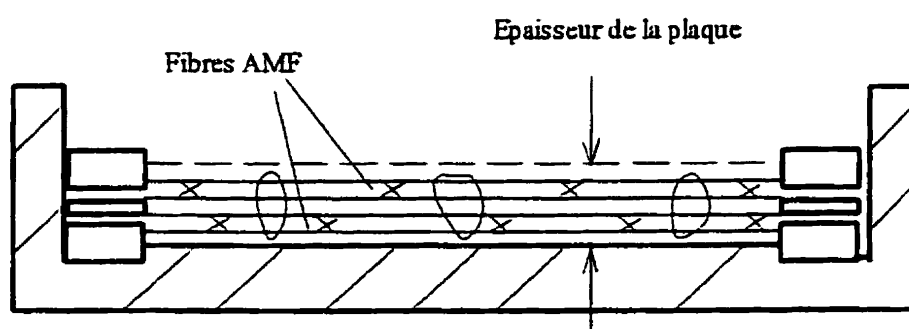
Vue de coupe du moule utilisé pour la fabrication des composites-AMF.
